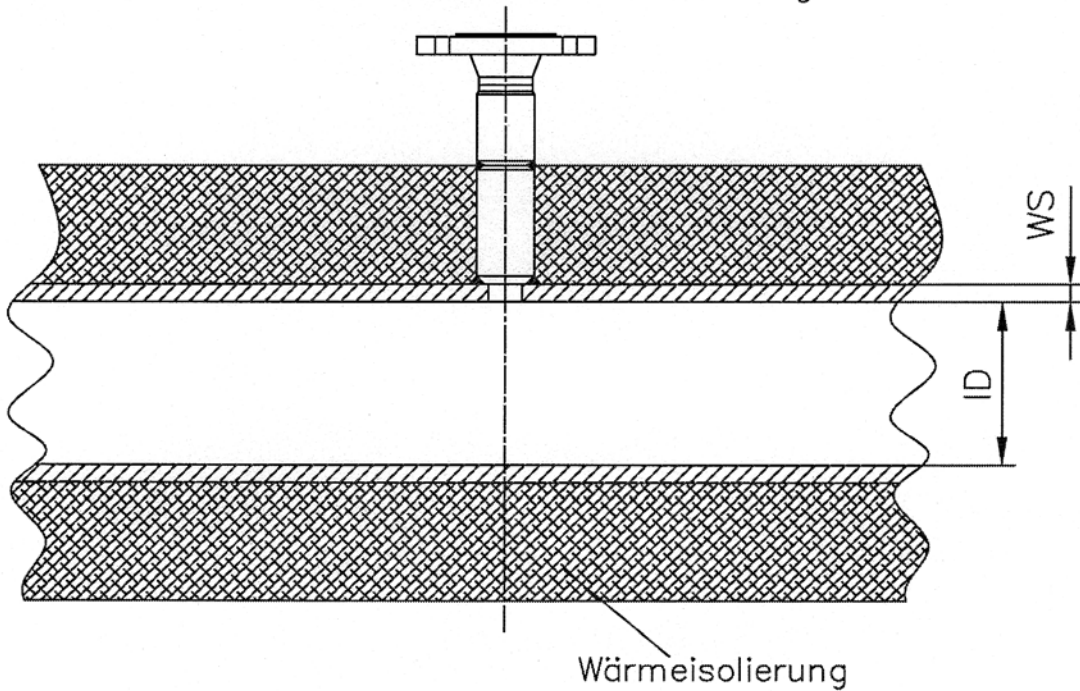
Einschweißverschraubung für IBR-25/26 aus 1.4571.
